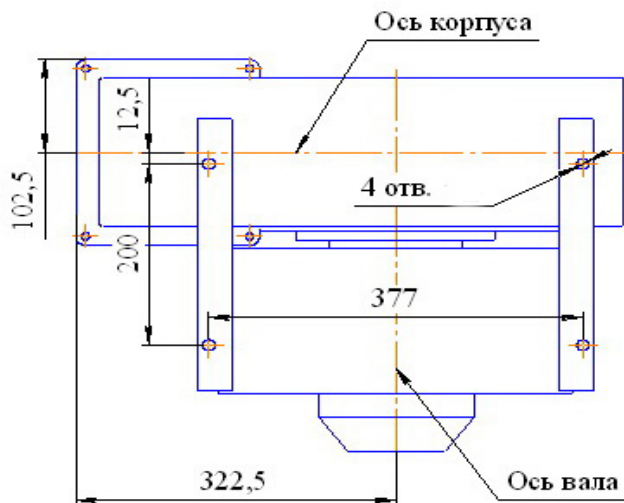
Вентиляторы ВРП-100-45-3,15. Установочные размеры.
